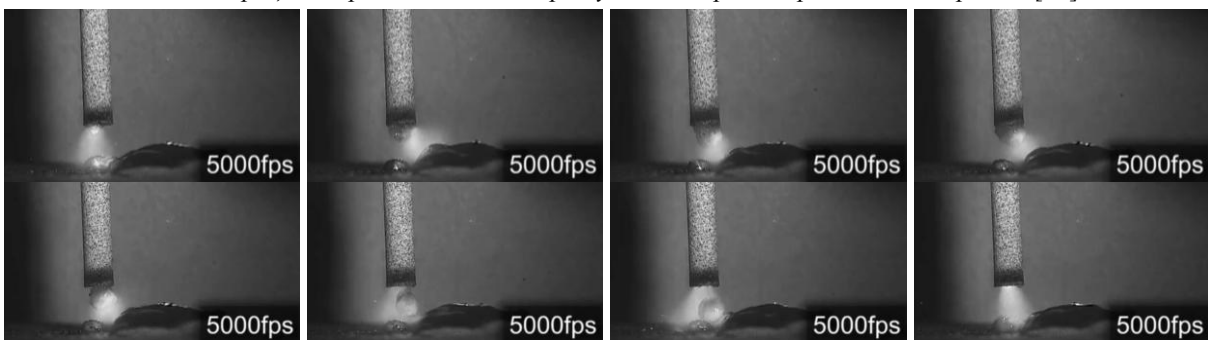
Процесс переноса металла при дуговой сварке расположенным вертикально покрытым электродом [15]
